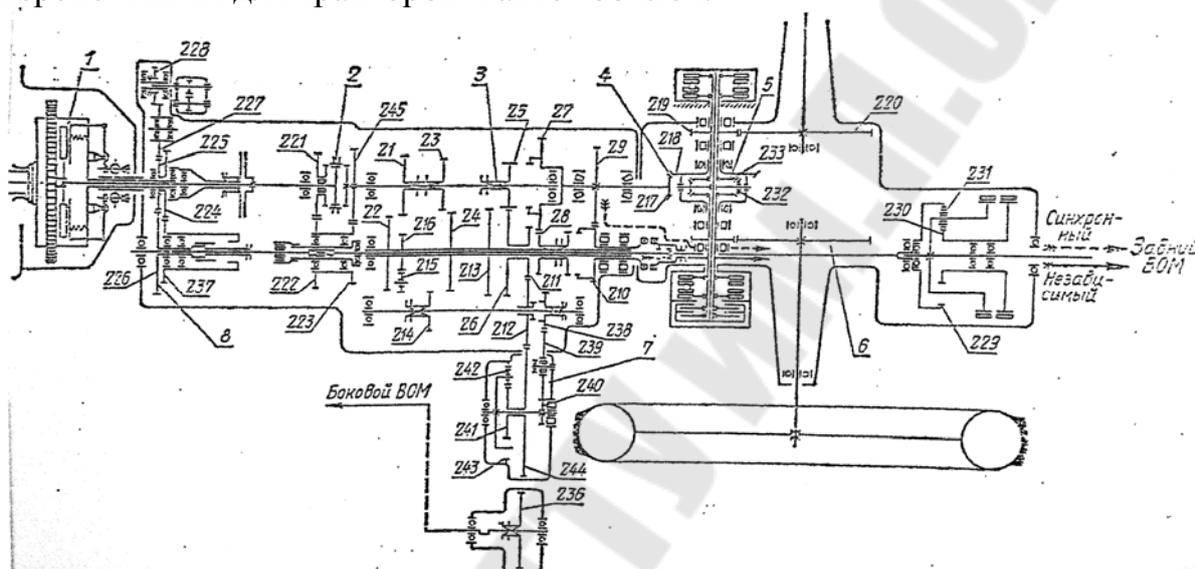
Кинематическая схема силовой передачи МТЗ-80:
